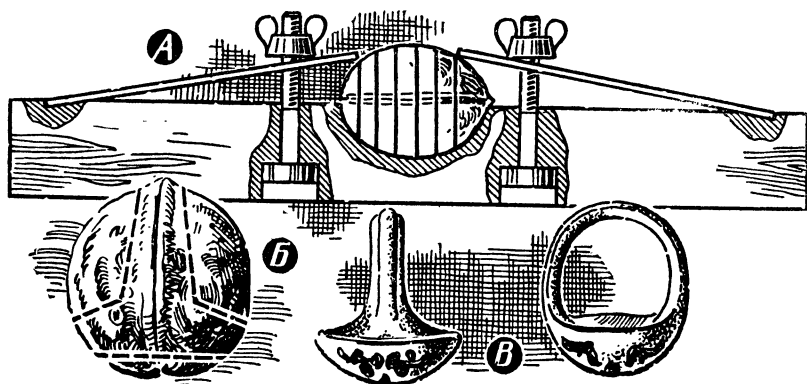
Приспособление для распиливания орехов: А — общий вид; Б — запилы при изготовлении кольца из грецкого ореха; В — обработка кольца.
